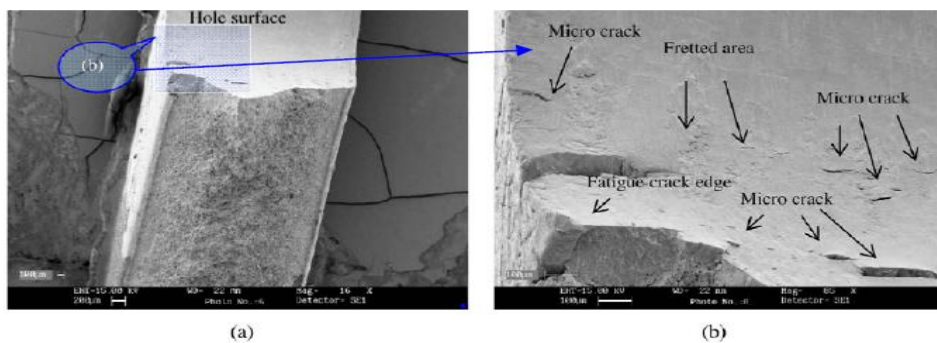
Sections fracturées après essai de fatigue pour différents éprouvettes [46].
